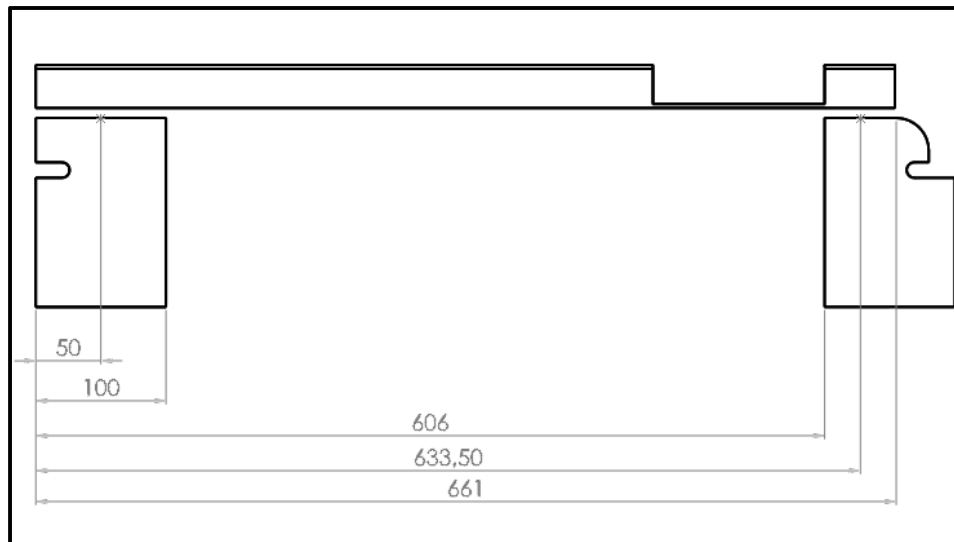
Dimensiones (en mm) de la estructura de soporte módulo 1
